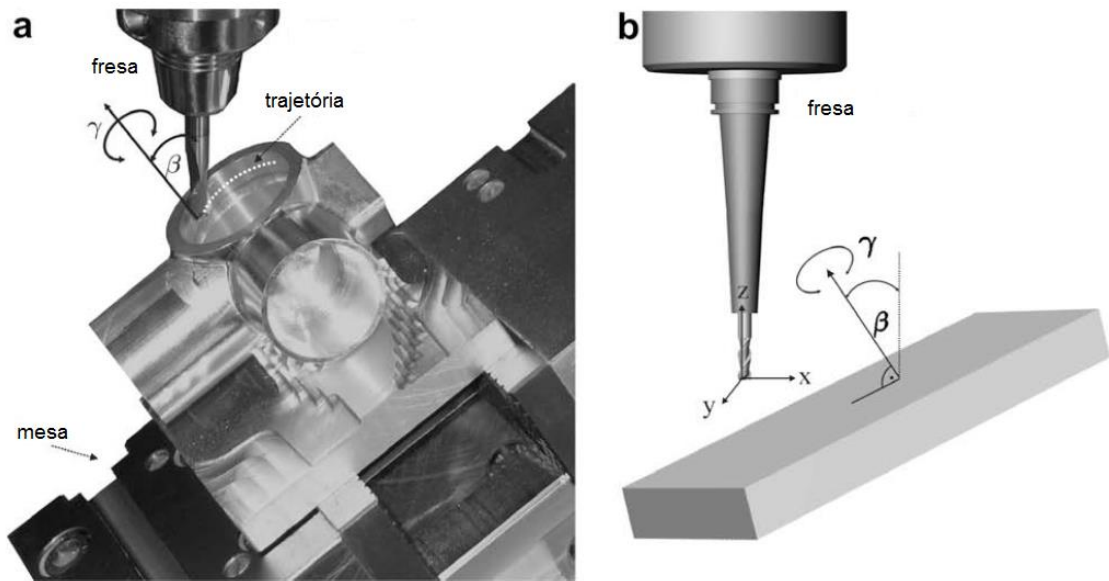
(a) Centro de usinagem cinco eixos e (b) movimentos de translação realizados pela ferramenta e movimentos de rotação realizados pela mesa (adaptado de KERSTING e ZABEL, 2009).
